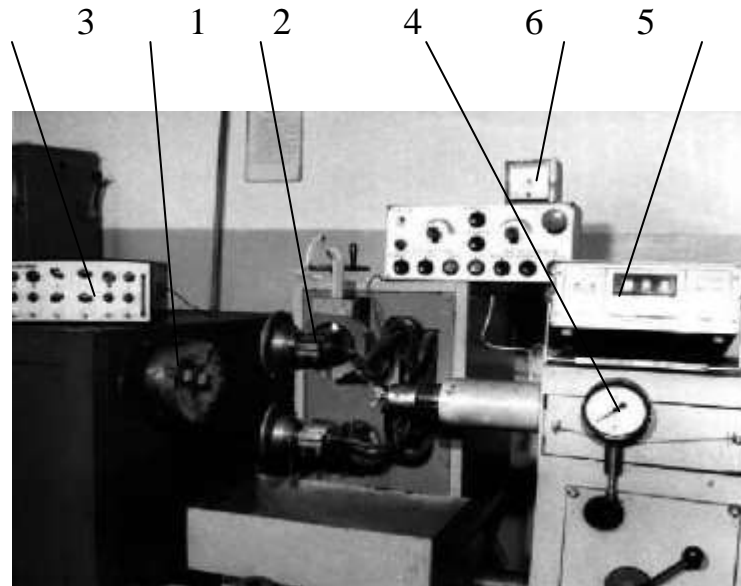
Установка для контактного наварювання композиційних стрічок
